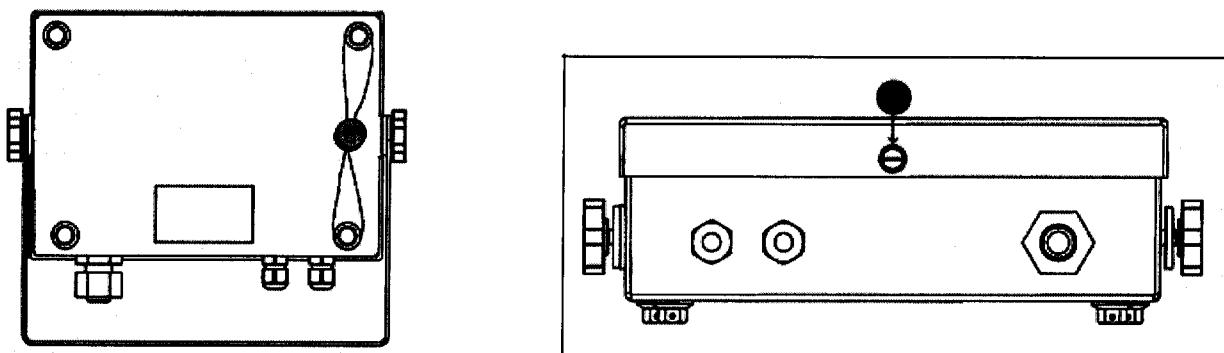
Примеры пломбировки корпуса терминалов
